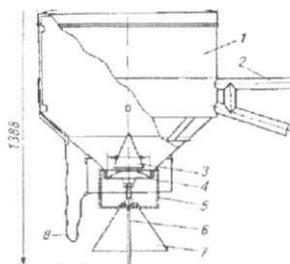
Кормушка клапанная: 1- бункер; 2-кронштейн; 3- разгрузочный конус; 4- грибовидный клапан; 5- кожух; 6- стержень; 7- отражатель; 8- привязь
